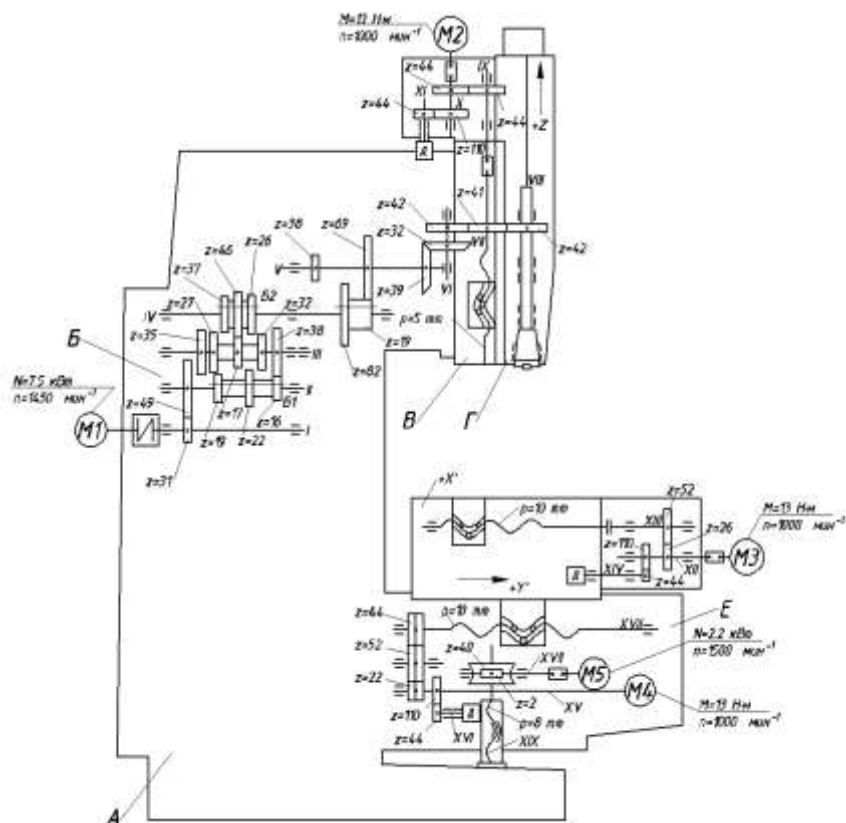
Кинематическая схема вертикально-фрезерного станка 6Р13Ф3-37
